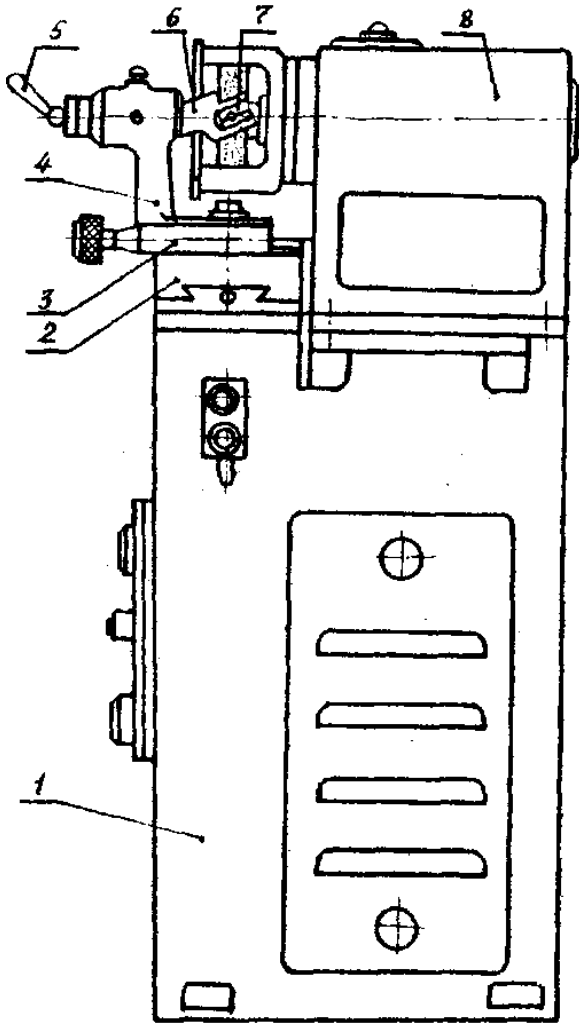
Верстат для заточування свердел моделі ЗБ652
